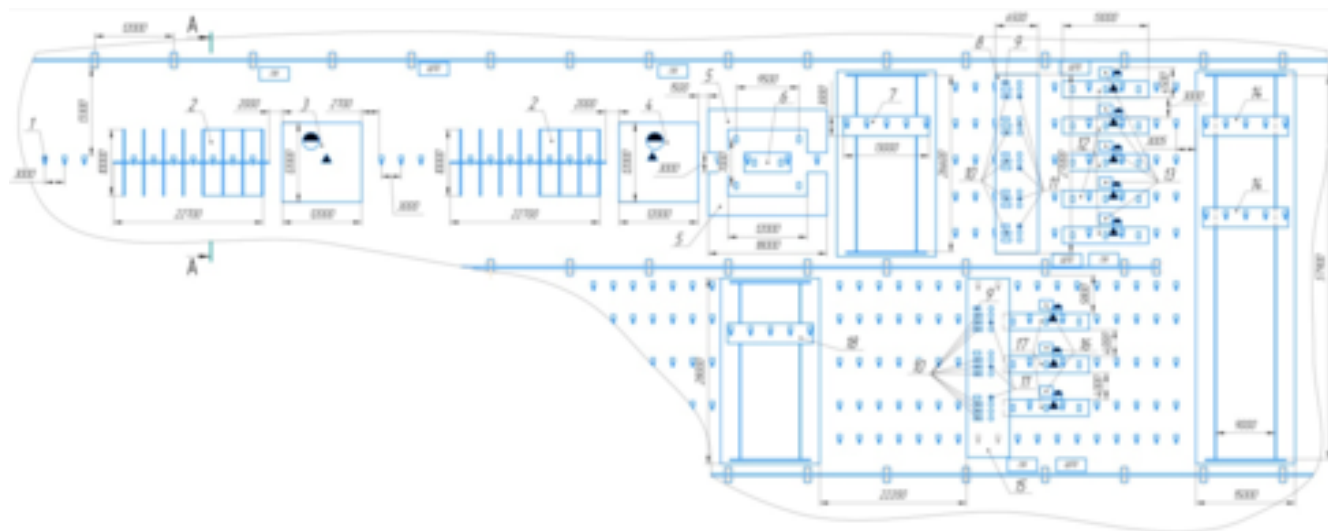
Вид участка сборки и сварки труб:
